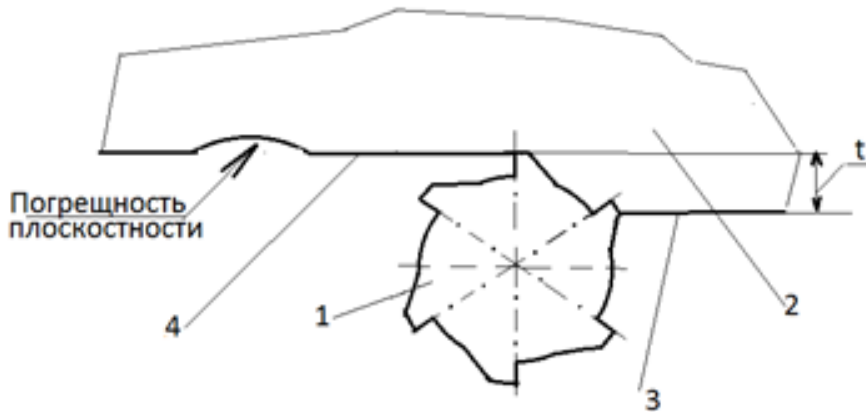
Типовая погрешность плоскостности при фрезеровании длиннокрюмочной концевой фрезой: 1 - фреза; 2 - деталь; 3 - обрабатываемая поверхность; 4 - обрабатываемая поверхность ж t - припуск под фрезерование.
